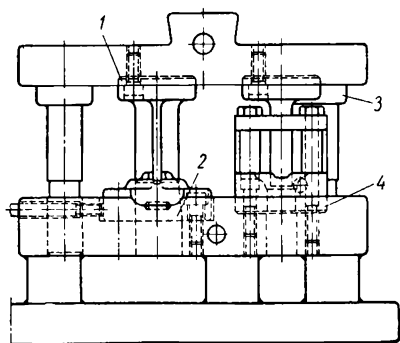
Последовательный штамп для обрезки и прошивки: 1 — обрезной пуансон; 2 — обрезная матрица; 3 — прошивочный пуансон; 4 — прошивная матрица
